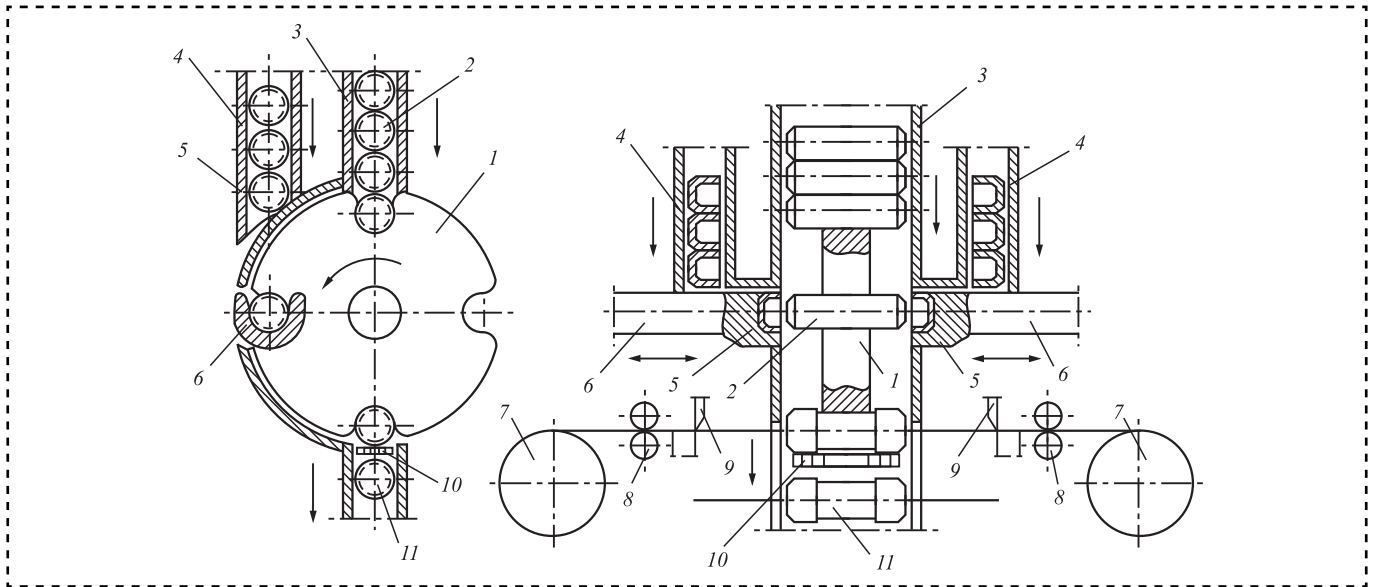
Сборочная установка 1-го типа для напрессовки на основание резистора колпачков и приварки контактных выводов:
